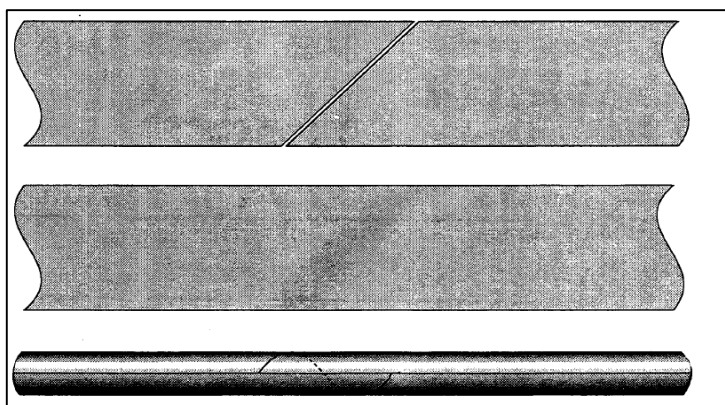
Lámina de acero soldada⁴⁵
